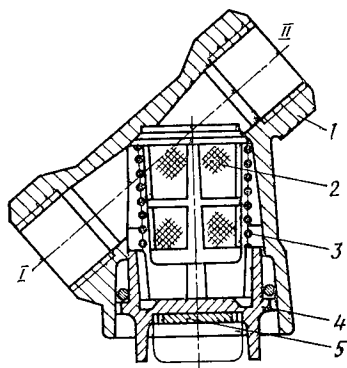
Магистральный фильтр: I и II — выводы; 1 — корпус; 2 — фильтрующий элемент; 3 — пружина; 4 — крышка с седлом; 5 — стопорная пластина
